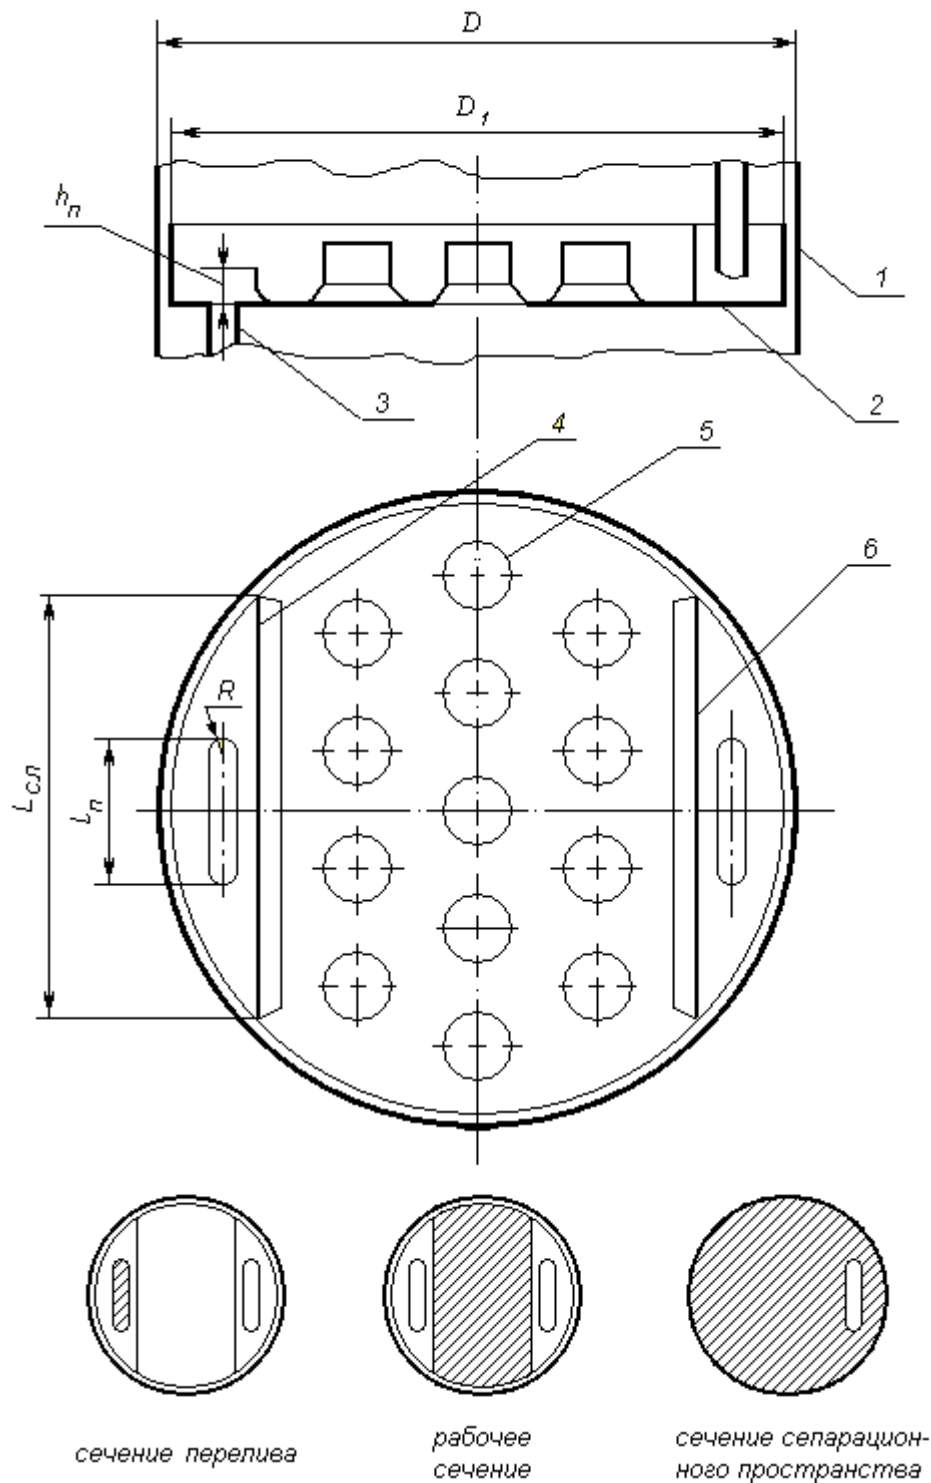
Устройство неразборных болтовых тарелок (болтики и детали крепления не показаны): 1 - стенка колонны, 2 - основание тарелки, 3 - сливной патрубок, 4 - переливная перегородка, 5 - паровой патрубок, 6 - входной порог; D - внутренний диаметр колонны, D_1 - внутренний диаметр тарелки $D_1 = D - 2\delta$ (где δ - толщина тарелки), h_n - высота тарелки, L_{cp} - длина перелива, l_n - длина переливного патрубка, R - полуширина переливного патрубка
